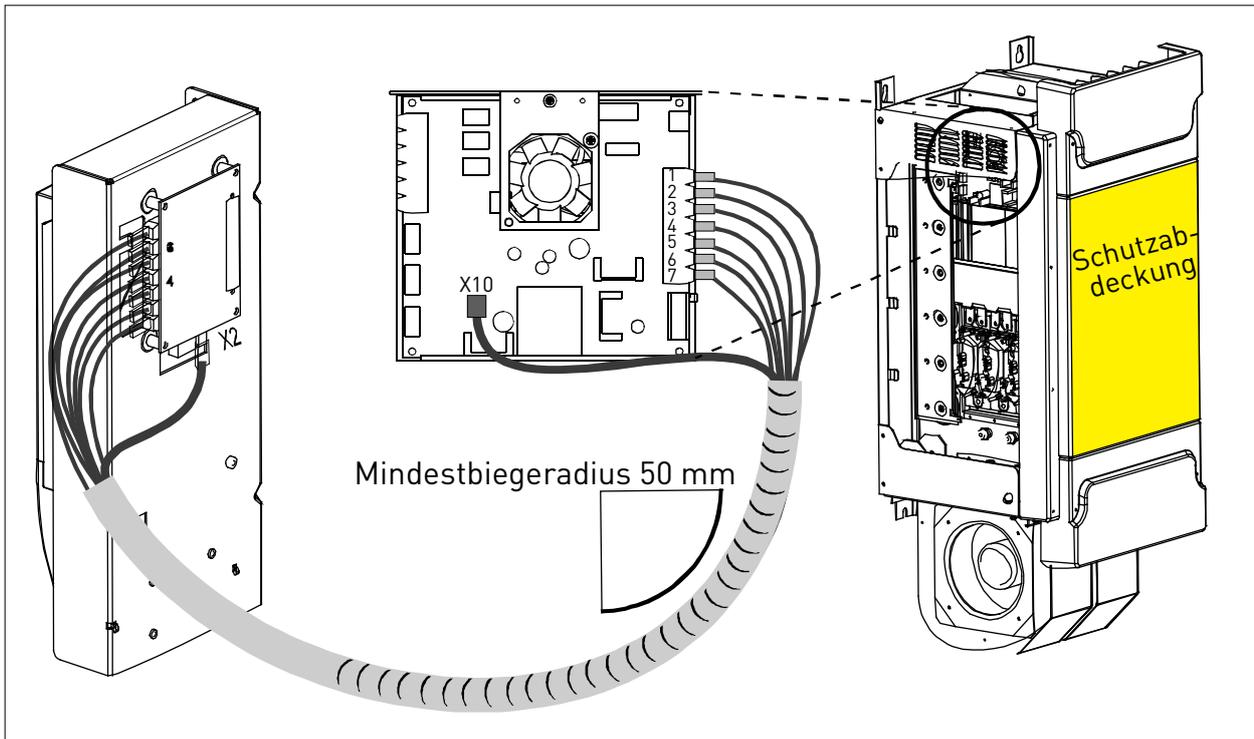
Steuereinheit auf schwenkbarem Montagegehäuse (nicht standardmäßig im Lieferumfang enthalten) am Schrankrahmen montiert, Baugrößen FR13 / FR14
